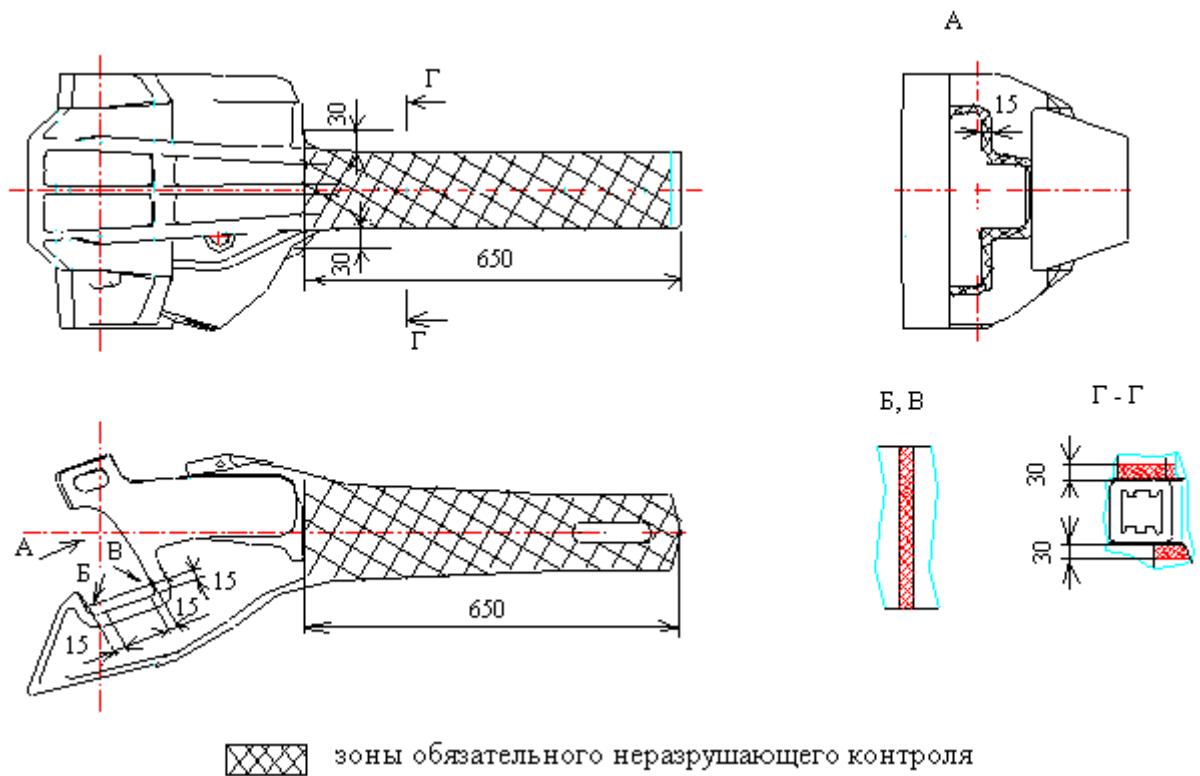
Зоны неразрушающего контроля на корпусе автосцепки СА-3
